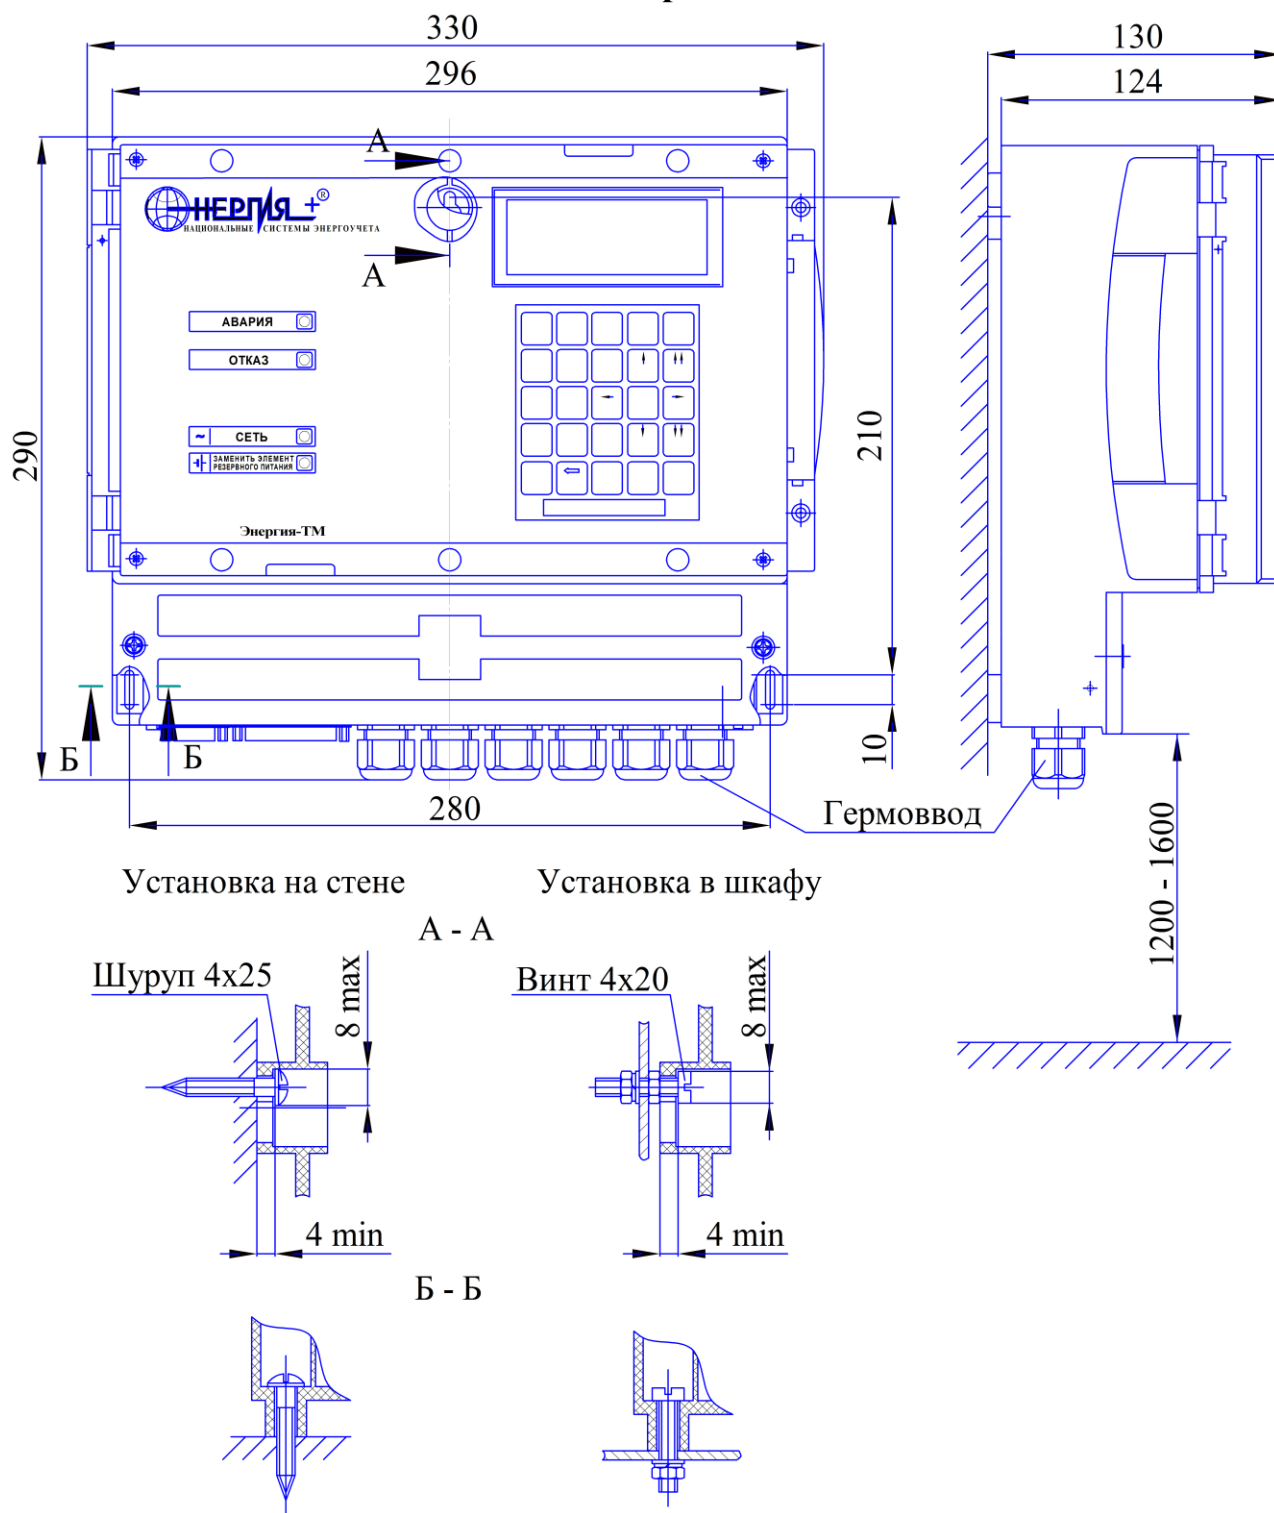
Габаритные и установочные размеры преобразователя
